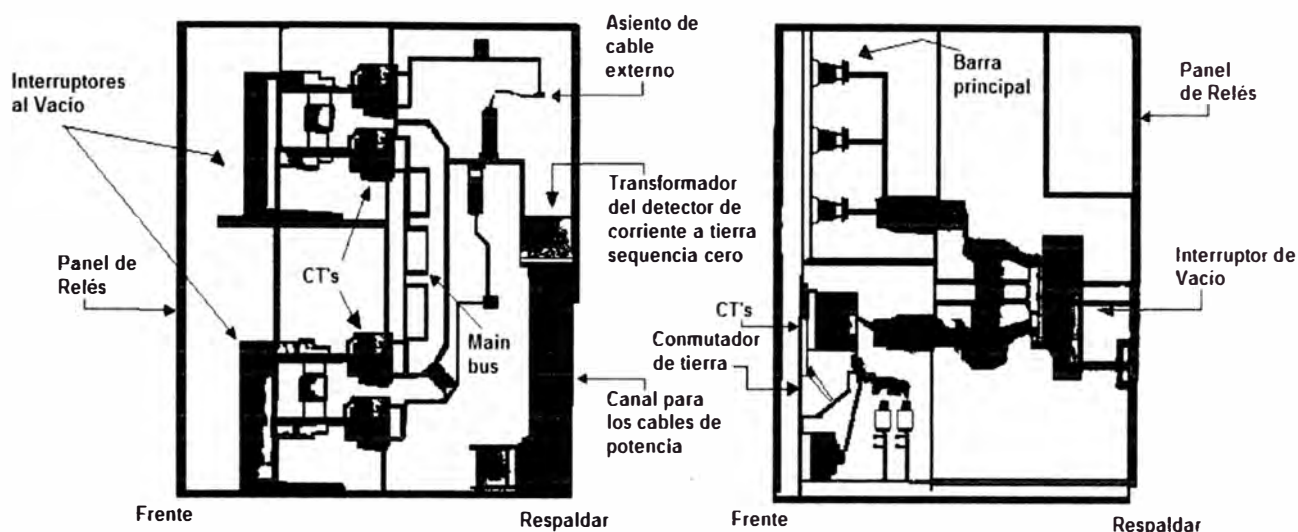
Celda ANSI a la izquierda y celda IEC a la derecha.
